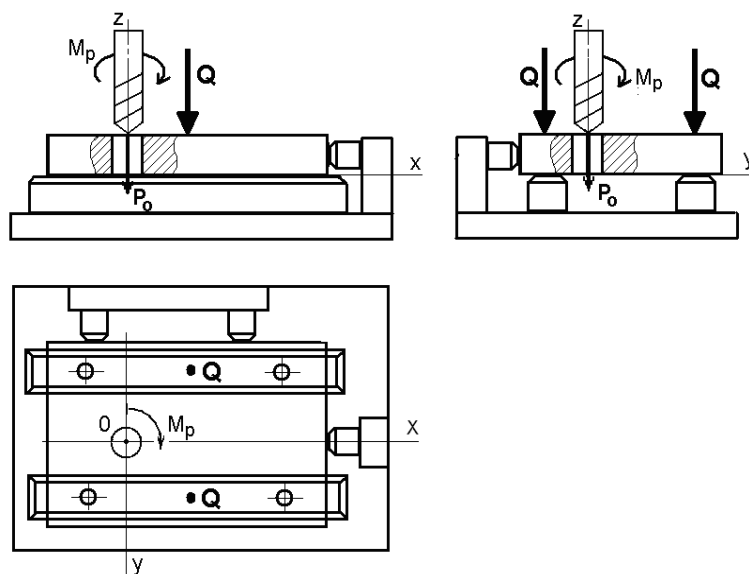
Приклад схеми закріплення заготовки у пристосуванні
